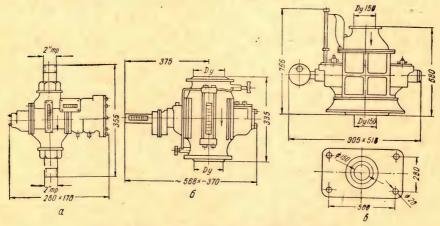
Габаритные размеры счетчиков: a - PC-25; 6 - PC-100; e - PC-600.
